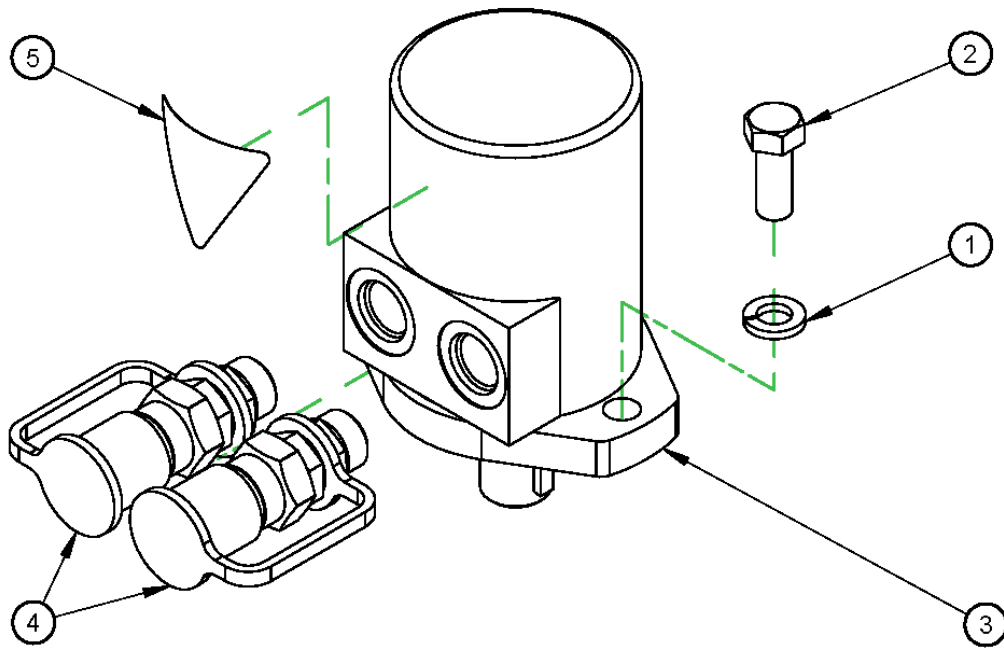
GROUPE CE DU MOTEUR PNEUMATIQUE (Réf 28614)
